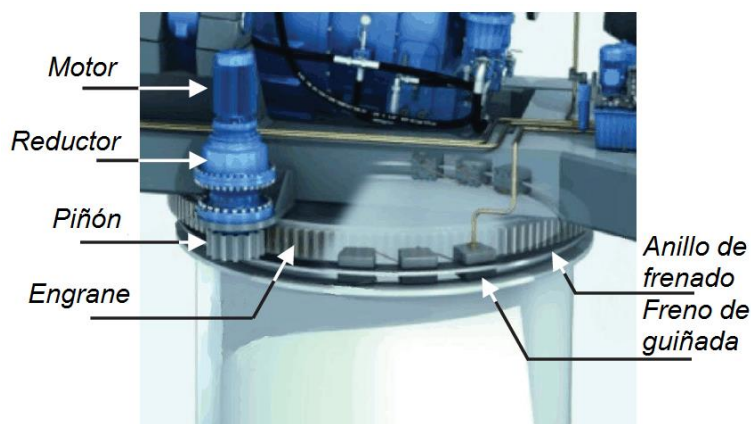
Sistema de guiñada de una turbina típica multimegawatt [16].
